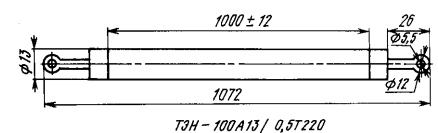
Габаритные, установочные и присоединительные размеры ТЭНа 100А13/0,5Т220
